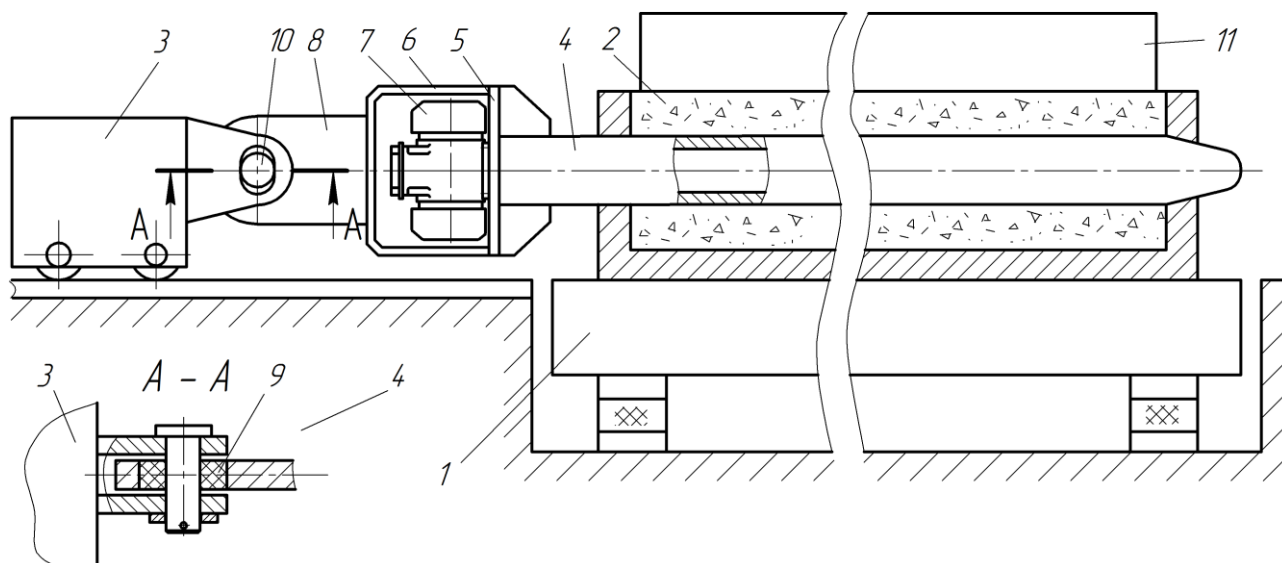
Схема установки для формования многопустотных панелей перекрытий с пригрузом.
